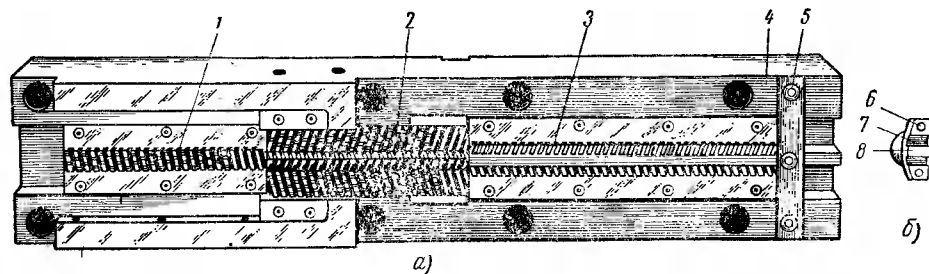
Наружная сборная протяжка для вертикально-протяжных станков, предназначенная для обработки подошвы подшипника
